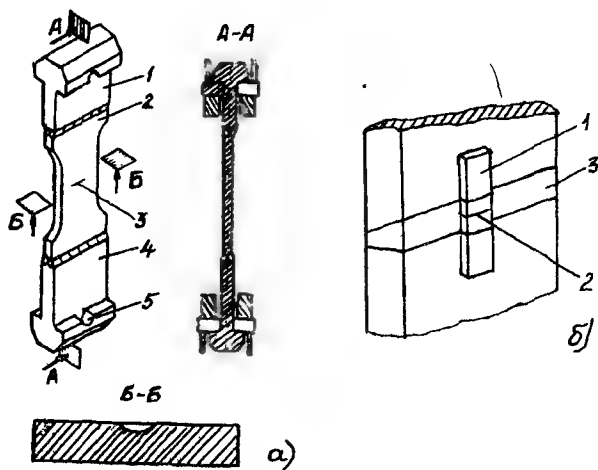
Конструкция плоского образца с поверхностной трещиной и схема его закрепления в нагружающем устройстве (а). Схема расположения выступа с надрезом, инициирующим возникновение поверхностной трещины (б)
